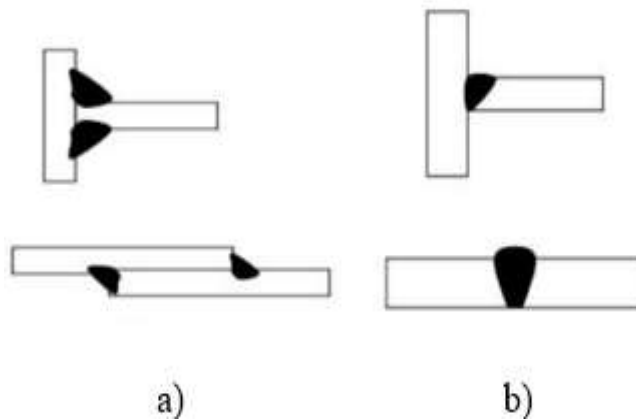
Ejemplos de conexiones soldadas: a) Conexión soldada tipo tope b) Conexión soldada tipo filete.
